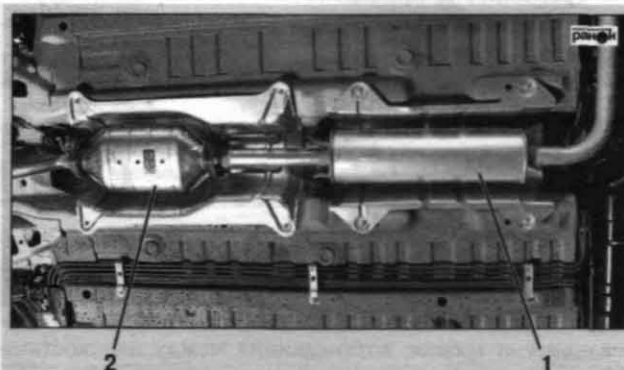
Передний глушитель и катализатор: 1 — передний глушитель; 2 — катализатор
